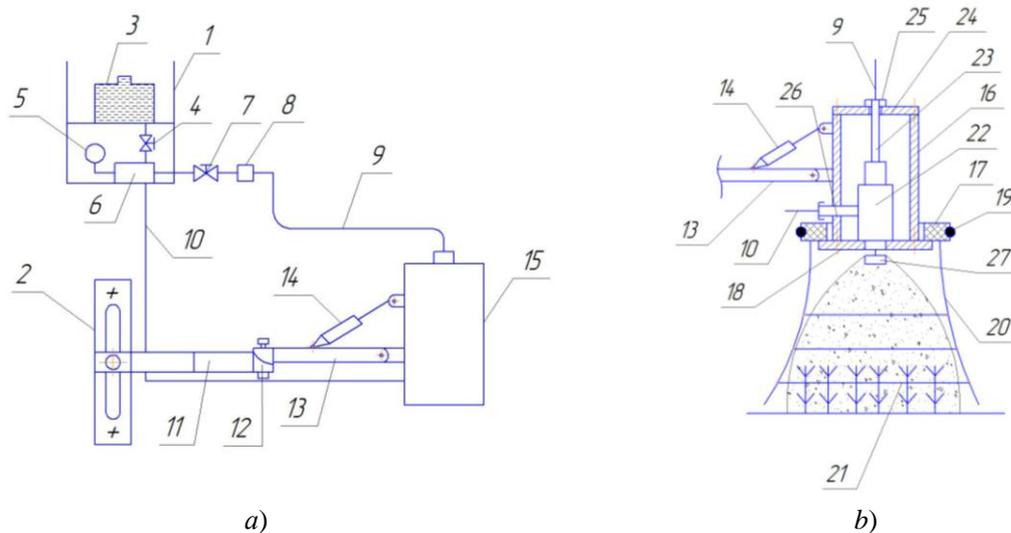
Конструктивно-технологическая схема устройства для внесения гербицида в приствольные полосы плодовых насаждений (а) и исполнительный механизм (b):
